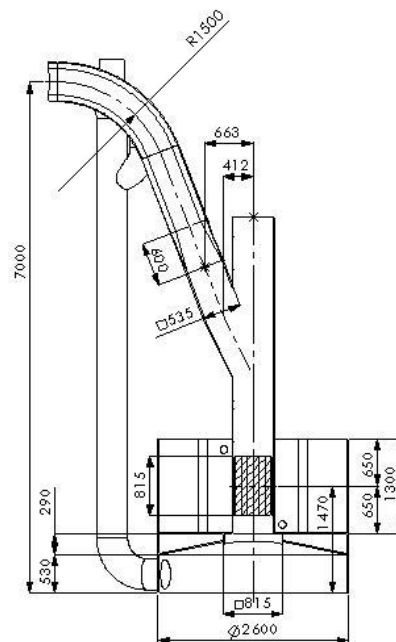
Corte lateral do RMB. (Dimensões em mm).
